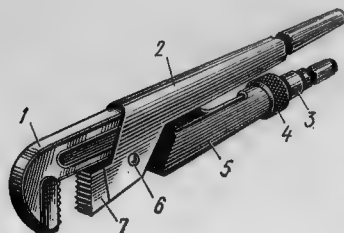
1 — рабочая часть (зев); 2 — корпус
